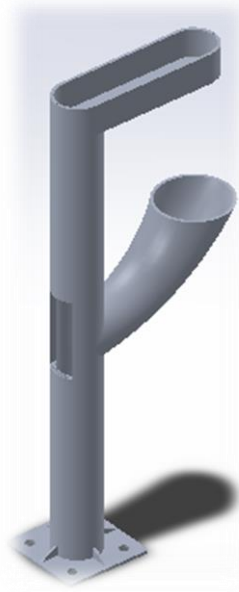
Pieza llamada Soporte Fuente: Elaboración propia
